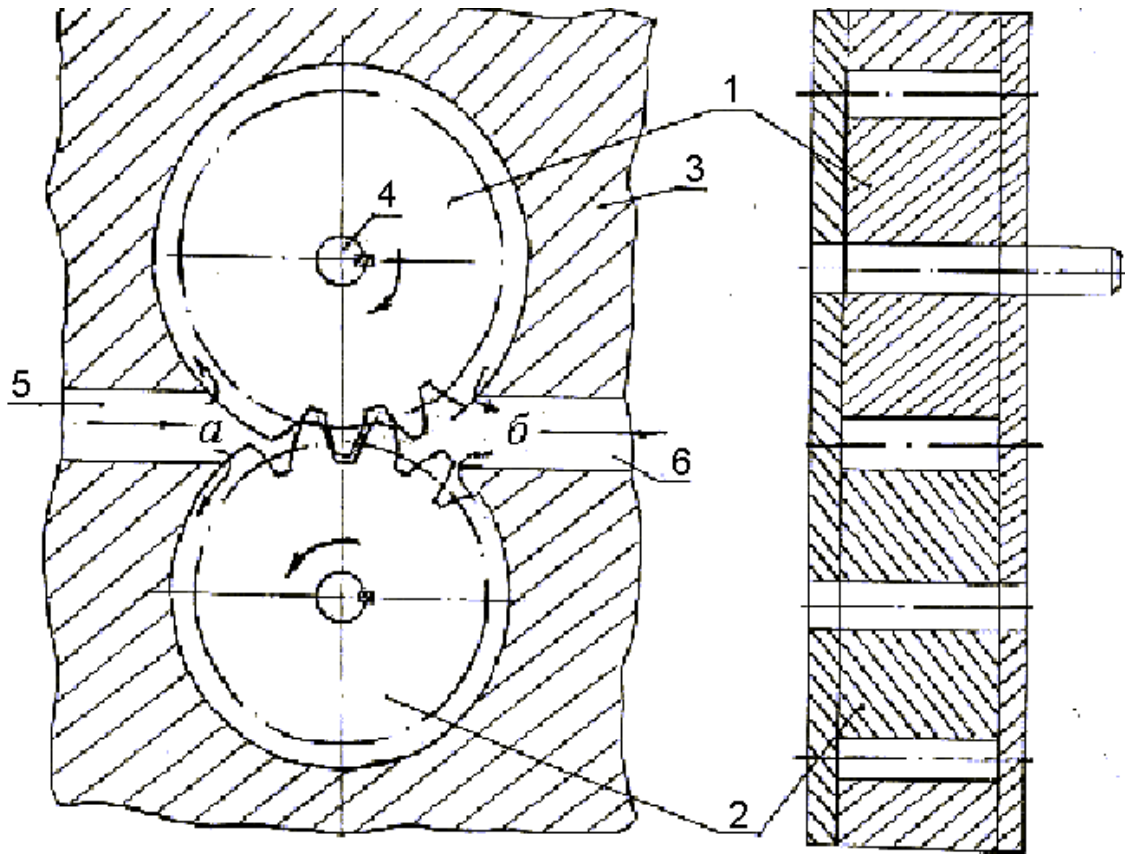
Конструктивная схема шестерённой гидромашины
